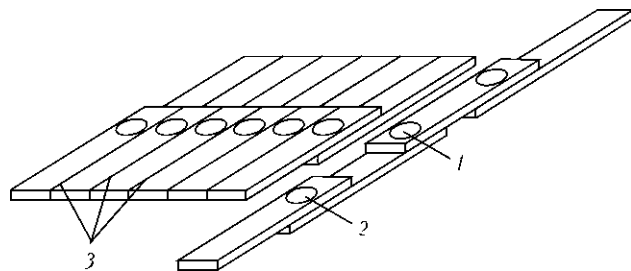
Схема подготовки образцов к испытаниям на разрыв: 1, 2 — сварные точки соответственно с проковкой и без нее; 3 — линии разреза
